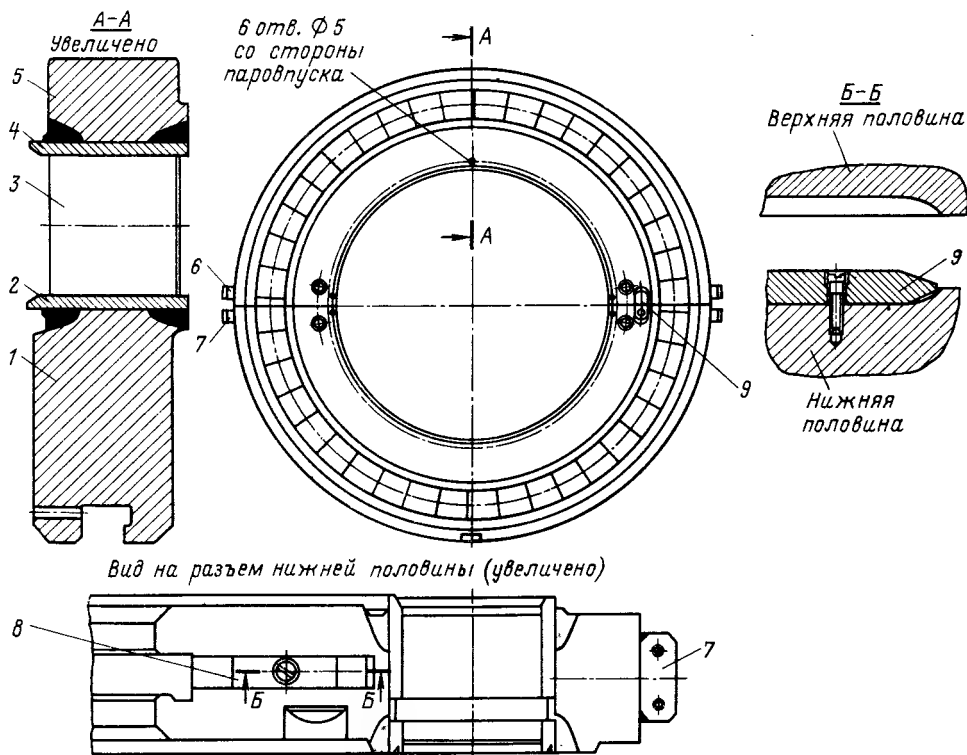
Сварная диафрагма для ЦВД турбин
